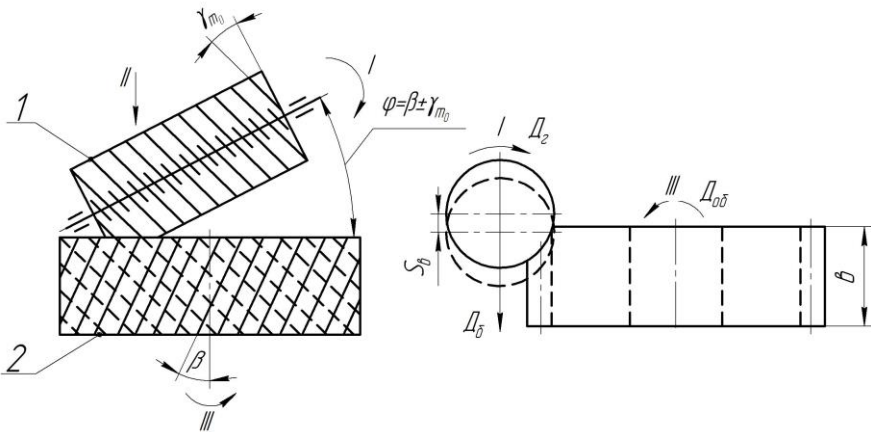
Схема установки фрезы относительно заготовки и основные движения при нарезании косозубого колеса
